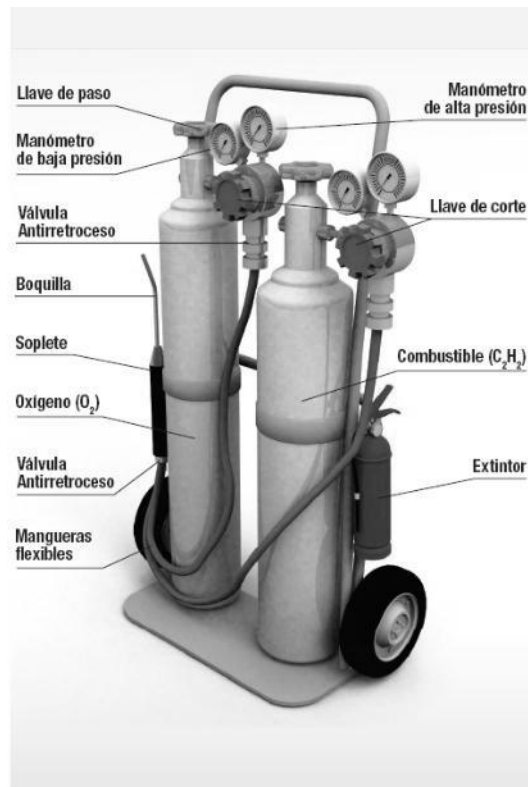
Esquema general del equipo utilizado en el soldado por flama.
